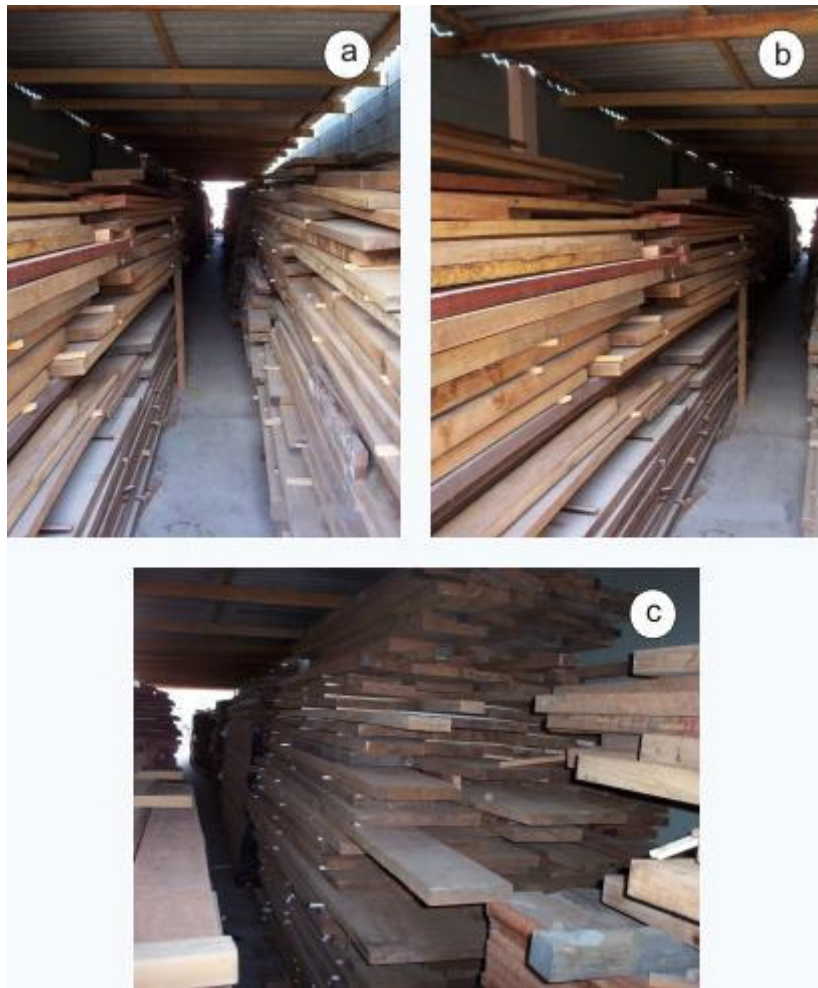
Tipo de empilhamento adotado pela empresa, detalhe do espaço para empilhamento da madeira (a), disposição dos separadores (tabiques) (b), defeitos decorrentes da estocagem e do empilhamento (c)
